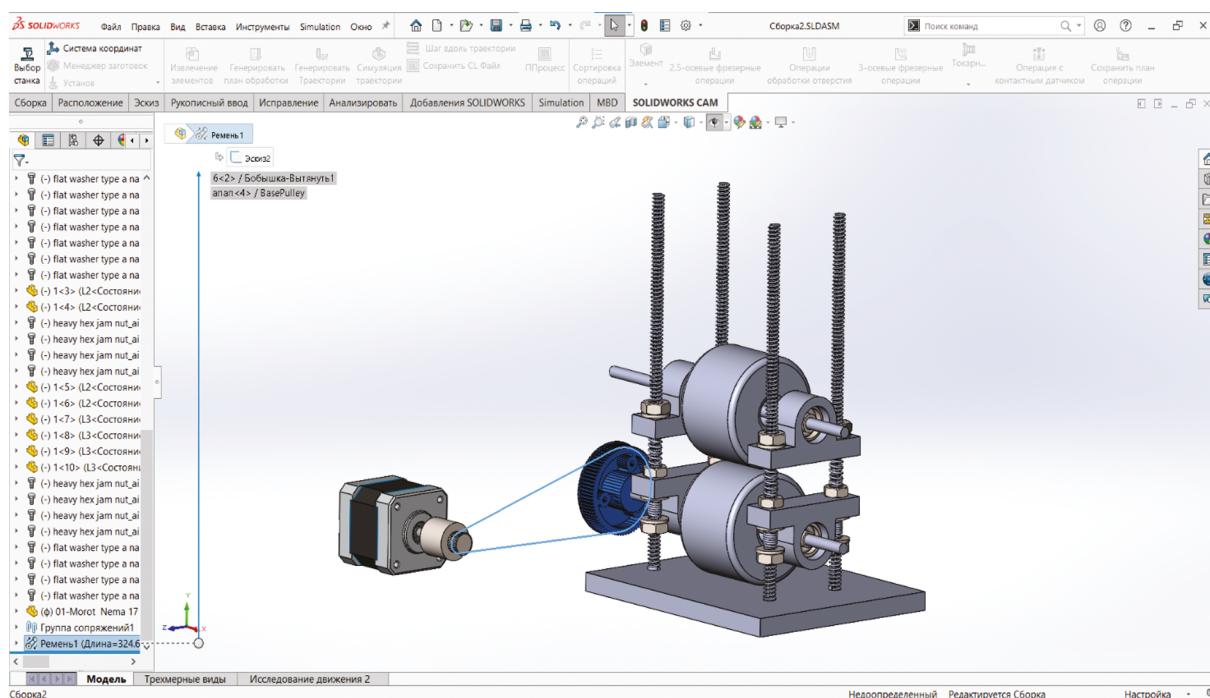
3D-модель сборки роликовой системы в приложении SolidWorks
